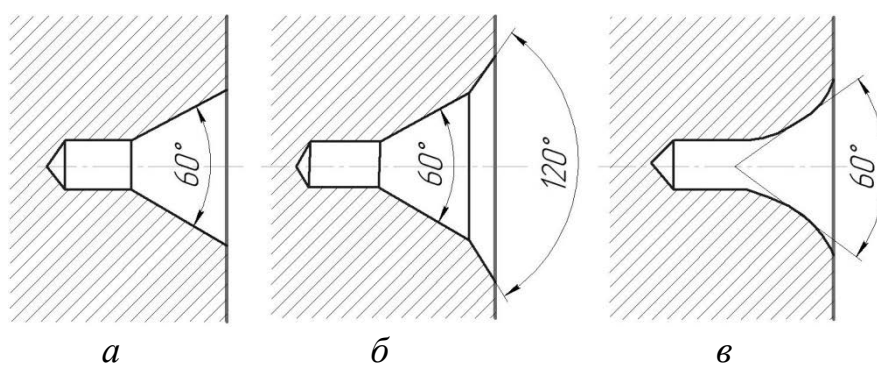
Виды центровых отверстий: а — без предохранительного конуса; б — с предохранительным конусом; в — с дугобразной образующей
